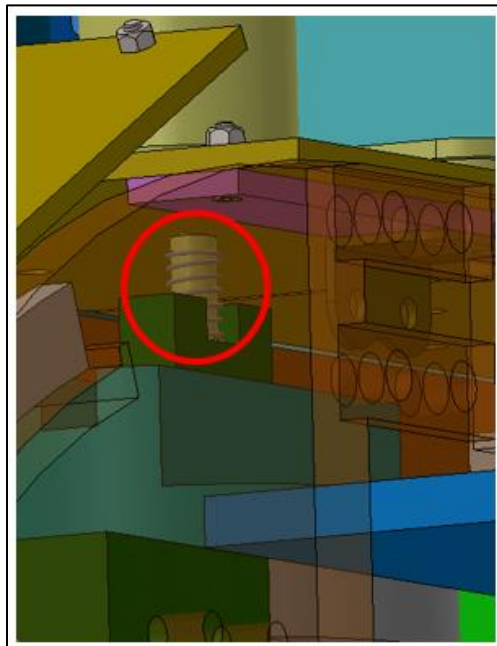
Pormenor de fixação do gabarito na paleta da passadeira indexada.
